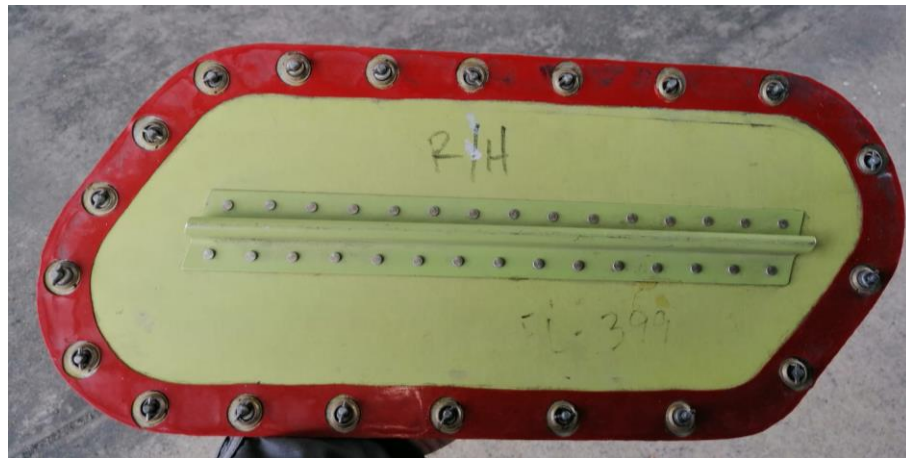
Tapa de inspección vista lateral izquierda. Fuente: Propia del autor.
